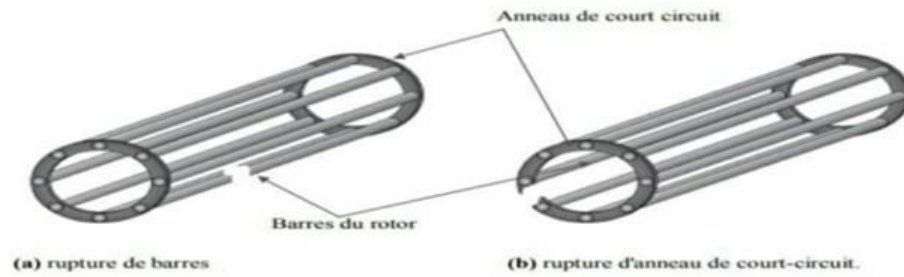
Défaut d'un rotor à cage d'écureuil
